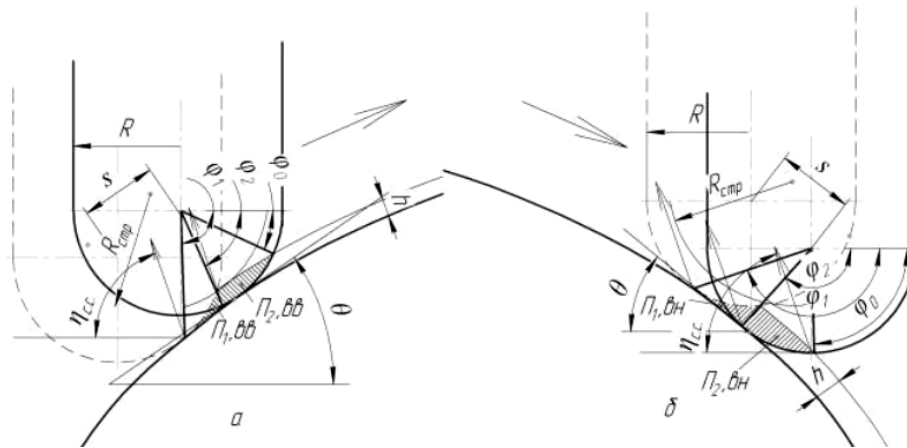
Геометрія шару, що зрізується, при обробці сферичною кінцевою фрезею
